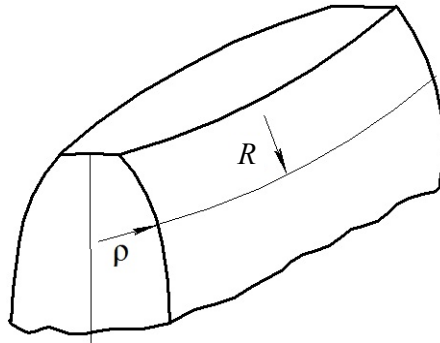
Зуб шестерни с криволинейными образующими боковых поверхностей
